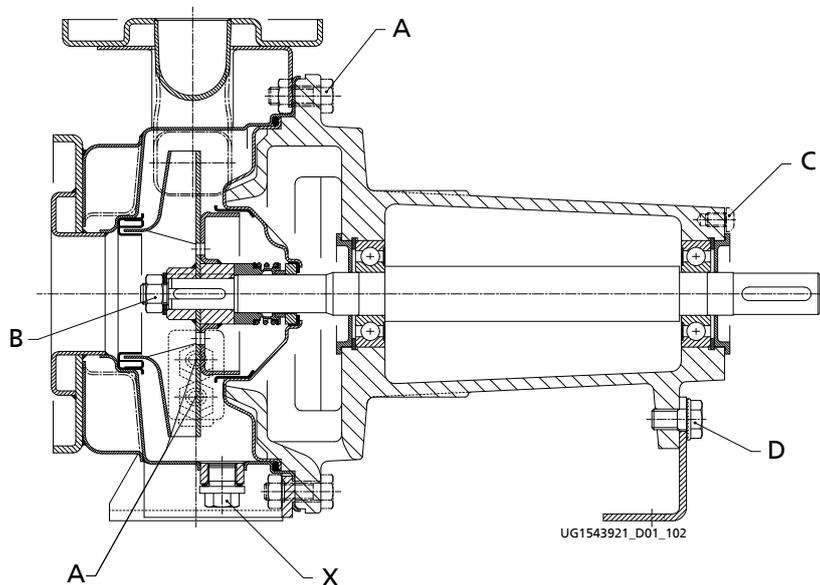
Posiciones de apriete de los tornillos, diámetro de rodete 125, 160, 200, excepto 065-050-200, 080-065-200, 100-080-200
